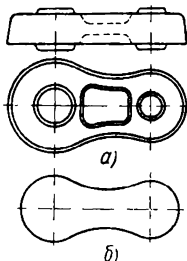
Поковка, требующая применения подкатки заготовки: а — поковка; б — заготовка
